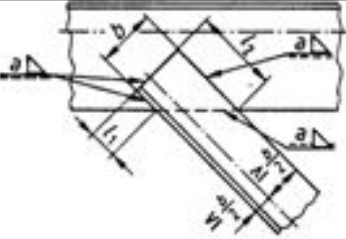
Схема расчетных сечений сварного соединения с угловым швом: 1 – сечение по металлу шва; 2 – сечение по металлу границы сплавления
